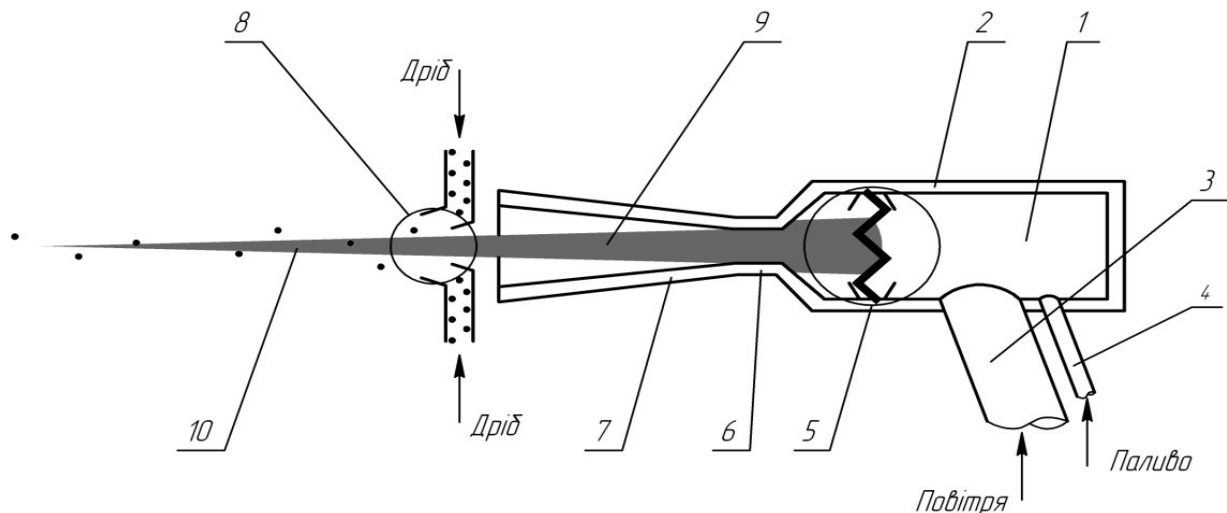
Принципова схема установки для газодинамічного очищення:
